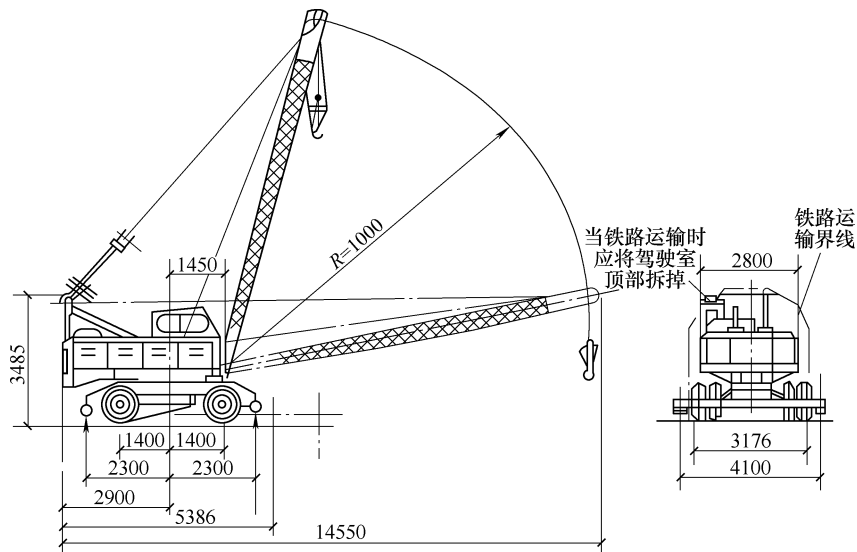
QLD16 型轮式起重机的外形 (单位: mm)
